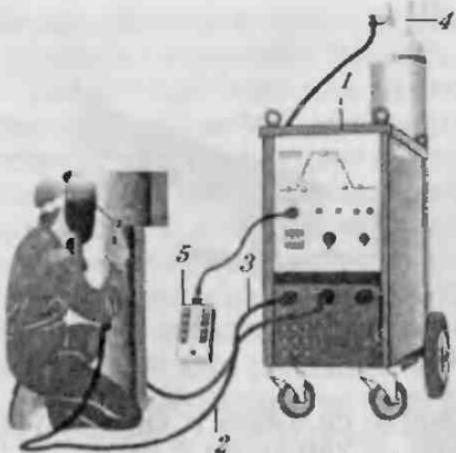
Сварочный пост для аргонодуговой сварки:
